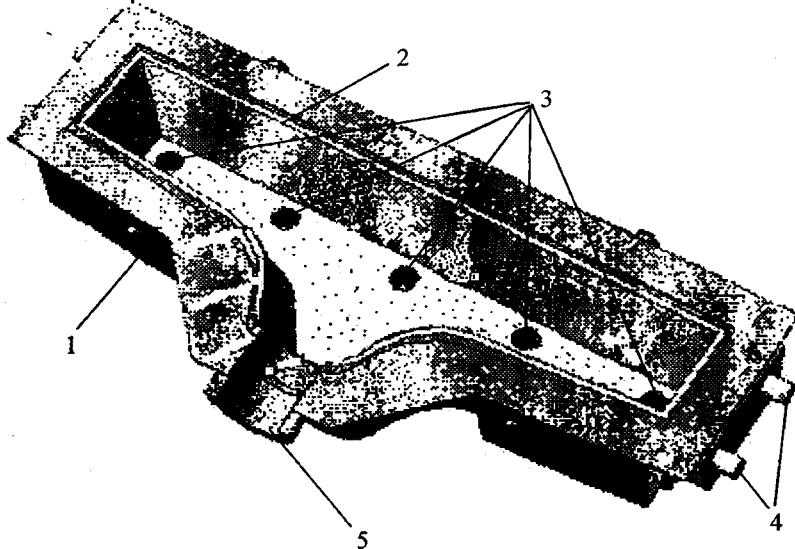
Схема \perp – образного промежуточного ковша пятиручьевой сортовой МНЛЗ: 1 – корпус; 2 – футеровка; 3 – разливочные отверстия; 4 – цапфы; 5 – сливной носок
